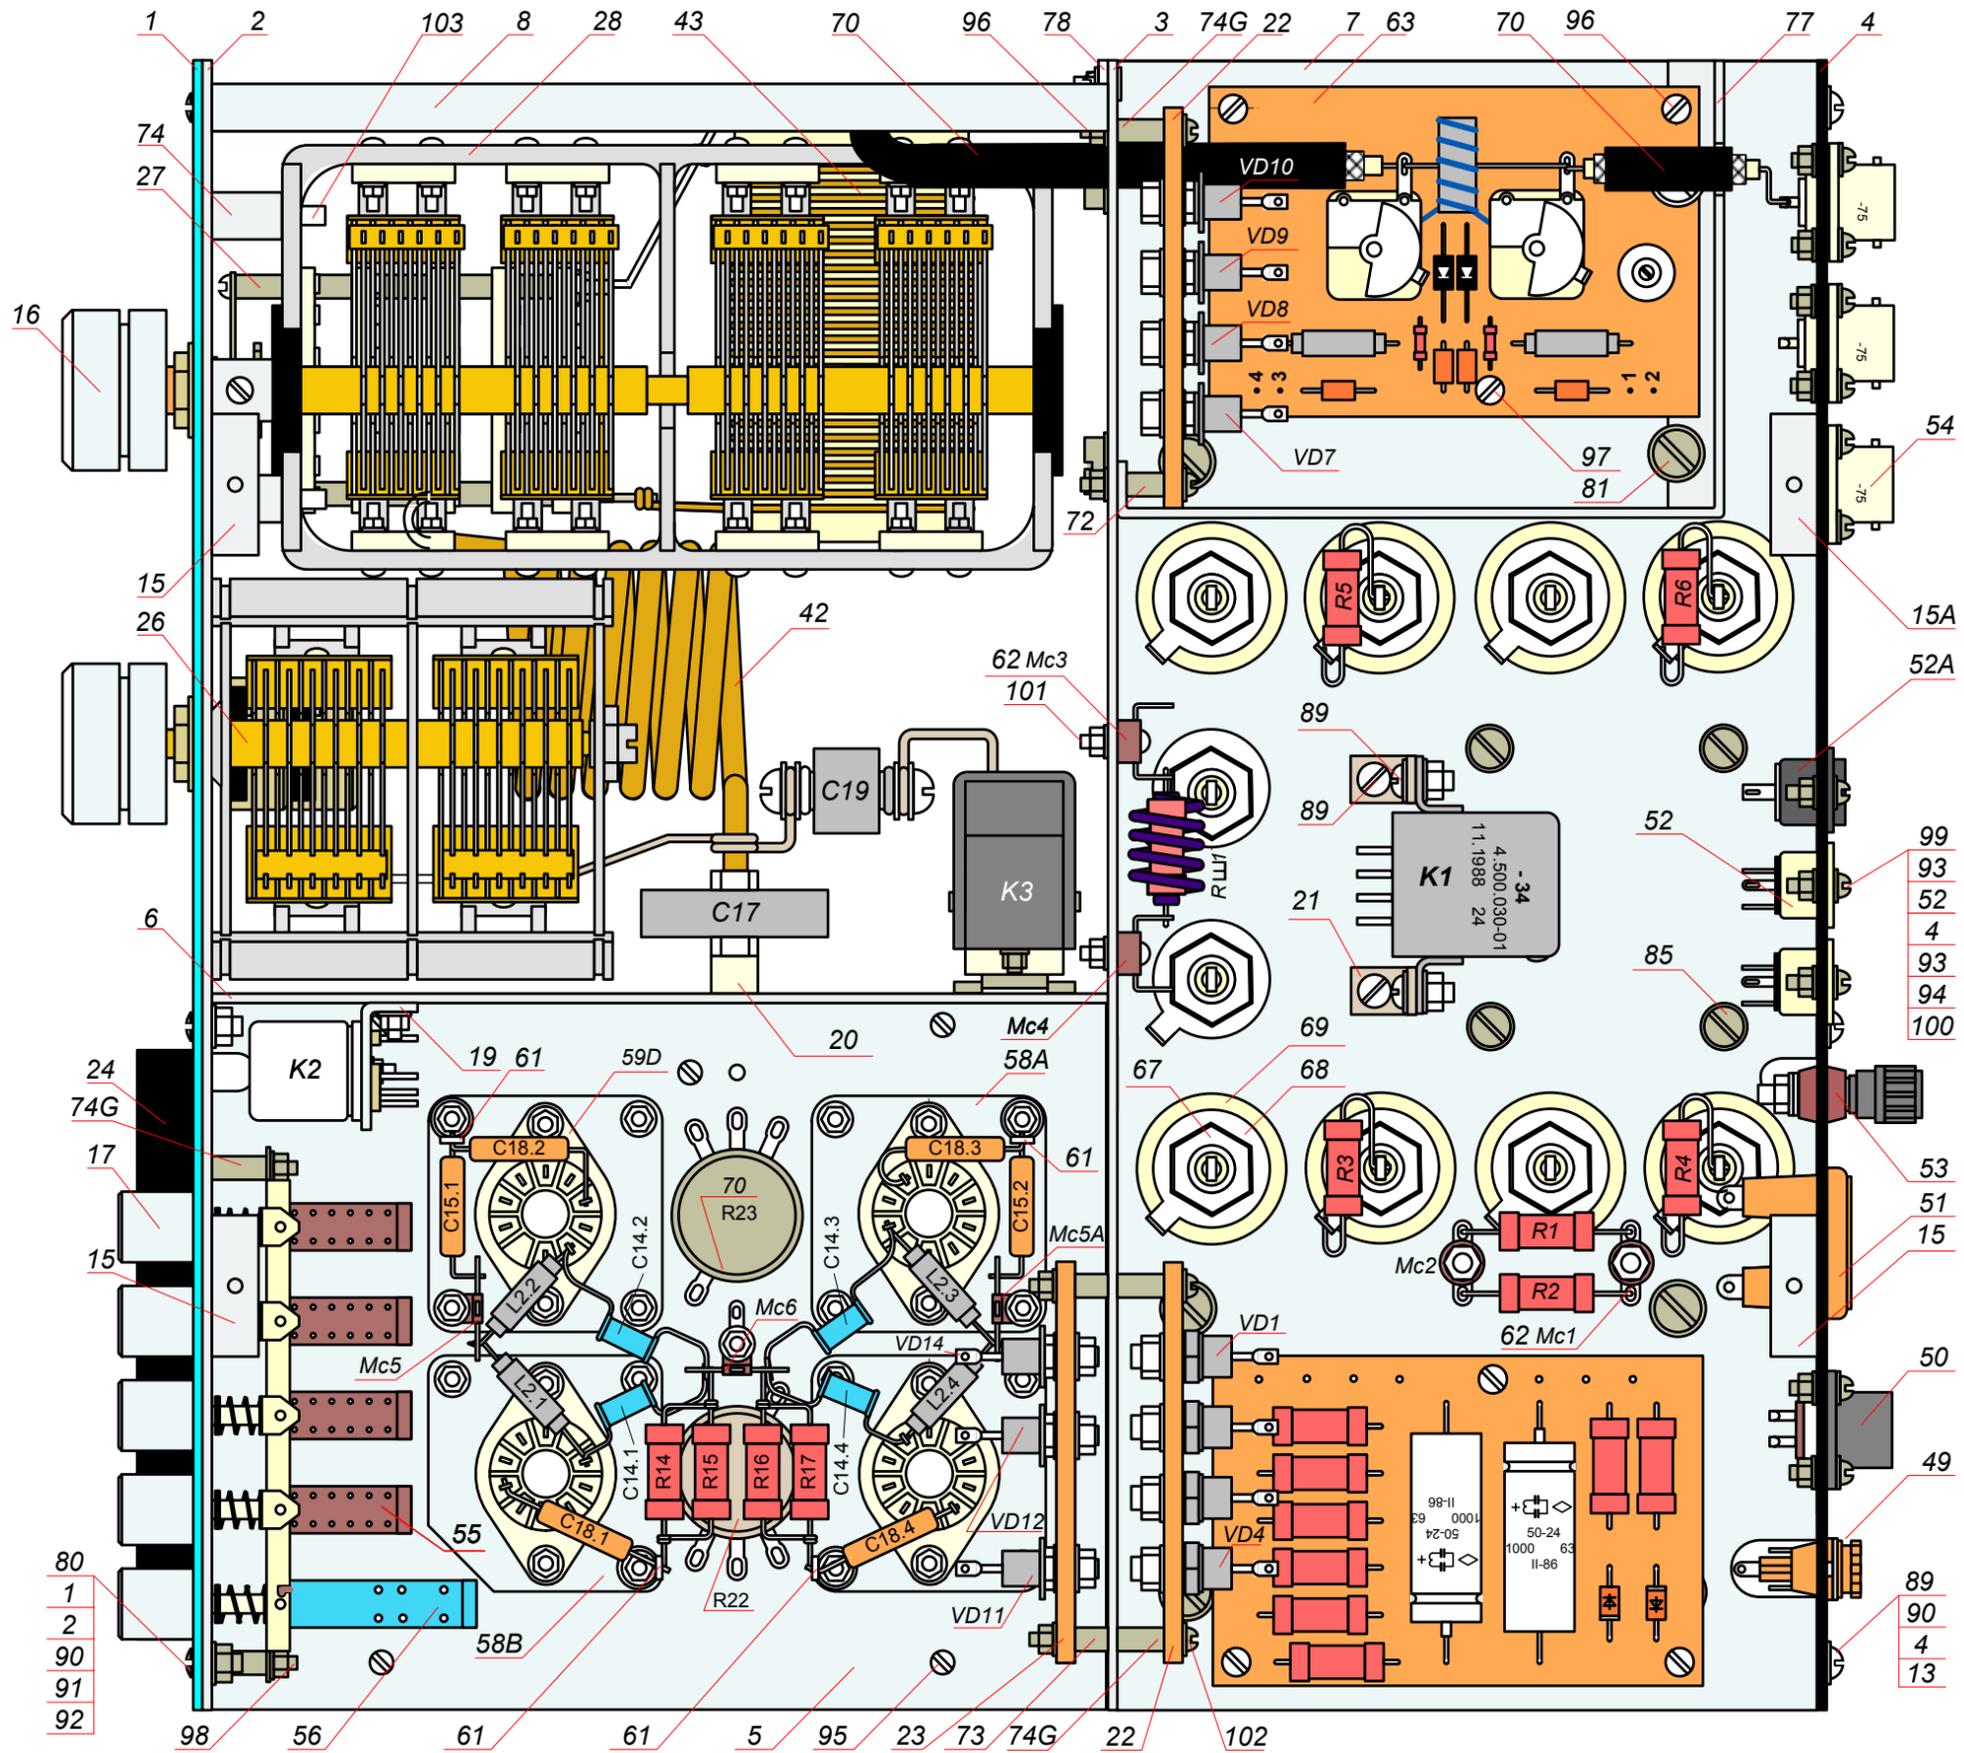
Е. Сборочный чертёж усилителя DVA-300Е. Вид сверху со снятыми верхней и нижней крышками.
